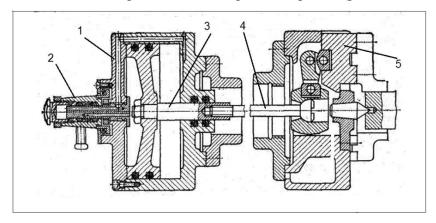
Пневмоцилиндр и патрон для токарного станка
